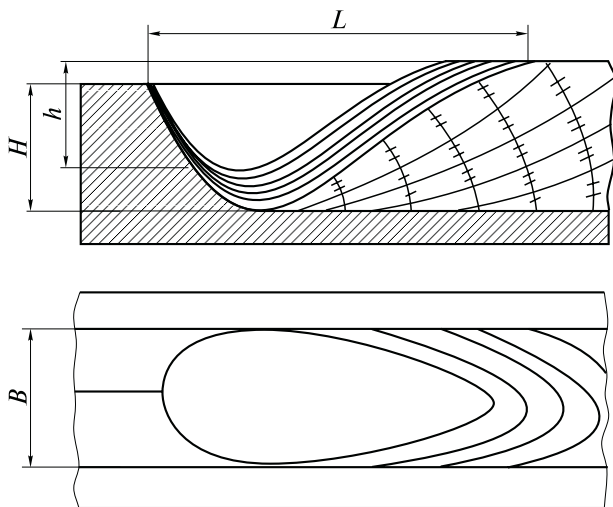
Параметры формы сварочной ванны:
